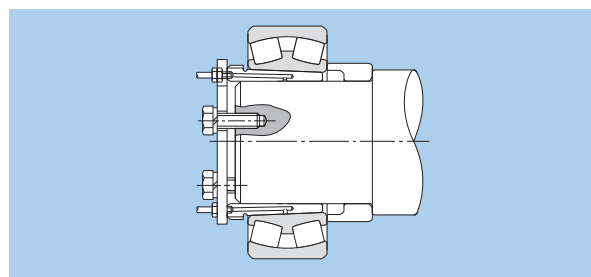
Instalação utilizando porca hidráulica com bucha de desmontagem
